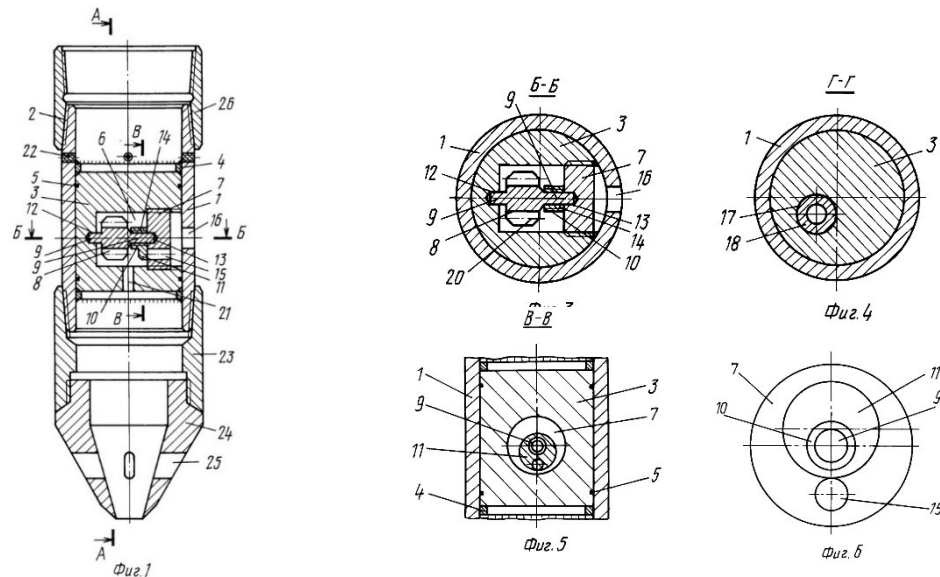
Вибробашмак цементируемой колонны на котором 1 – полый корпус, 2 – соединительные резьбы, 3 – цилиндр, 4 – приварные кольца, 5 – уплотненные резиновые кольца, 6 – цилиндрическая полость, 7 – легкоразбураиваемый диск, 8 – зубчатое колесо, 9 – вал, 10,11 – дебаланс, 12 – карман, 13 – карман, 14 – зубчатое шлицевое соединение, 15 – эксцентричное отверстие, 16 – отверстие, 17 – продольный канал, 18 – ось сопла, 19 – уплотненное кольцо, 20 – зубчатое колесо, 21 – осевой канал, 22 – предохранительные пробки, 23 – утолщенный патрубок, 24 – направляющая пробка, 25 – отверстия, 26 – муфта
